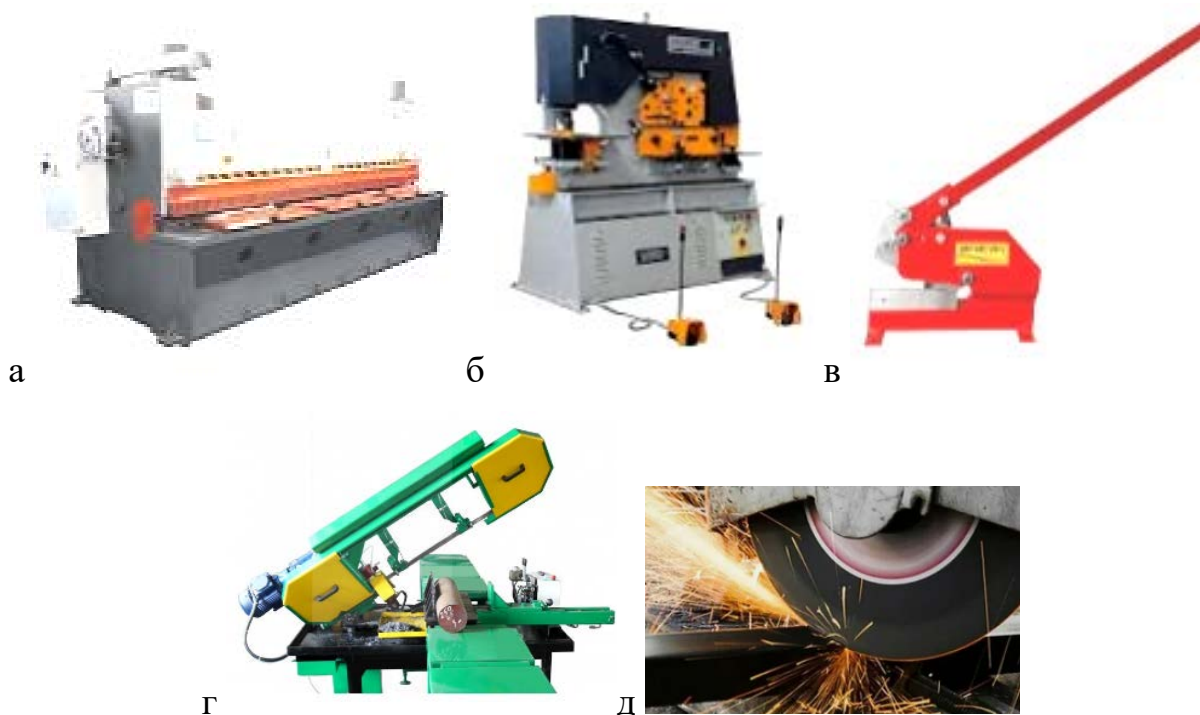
Гідравлічні гільйотинні ножиці (а), прес-ножиці (б), ручний верстат для різання металу товщиною до 5мм (в), стрічкова пилка по металу (г), дисковий верстат (д)
